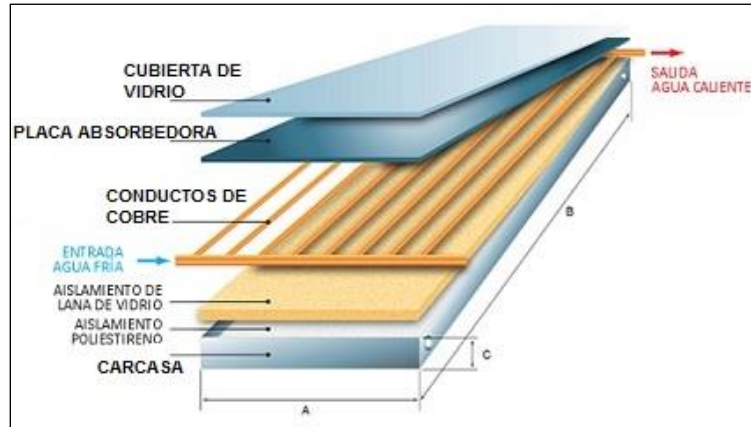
Componentes de un calentador solar plano. Fuente ingemecanica.com
